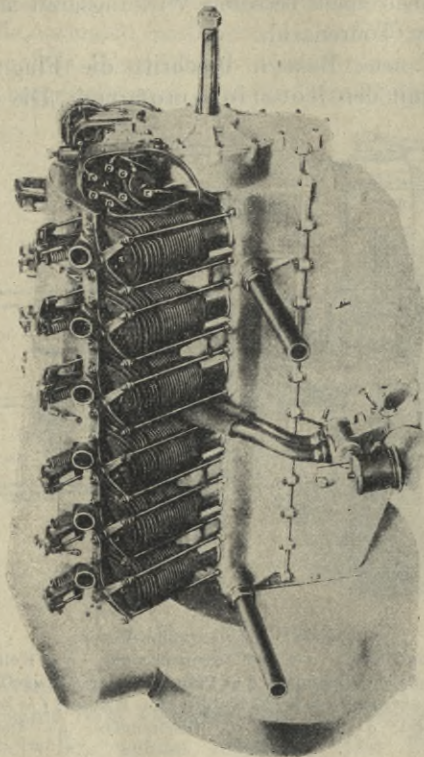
100 PS. 12 Zyl.-Renault-Motor.
